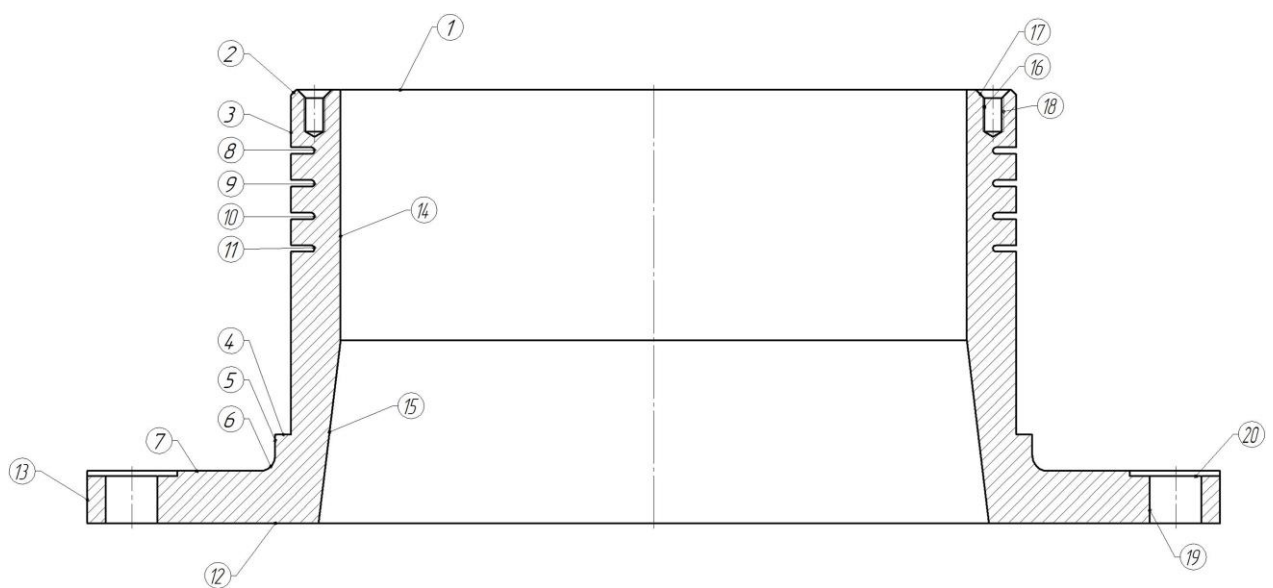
Нумерація поверхонь деталі “Стакан”
